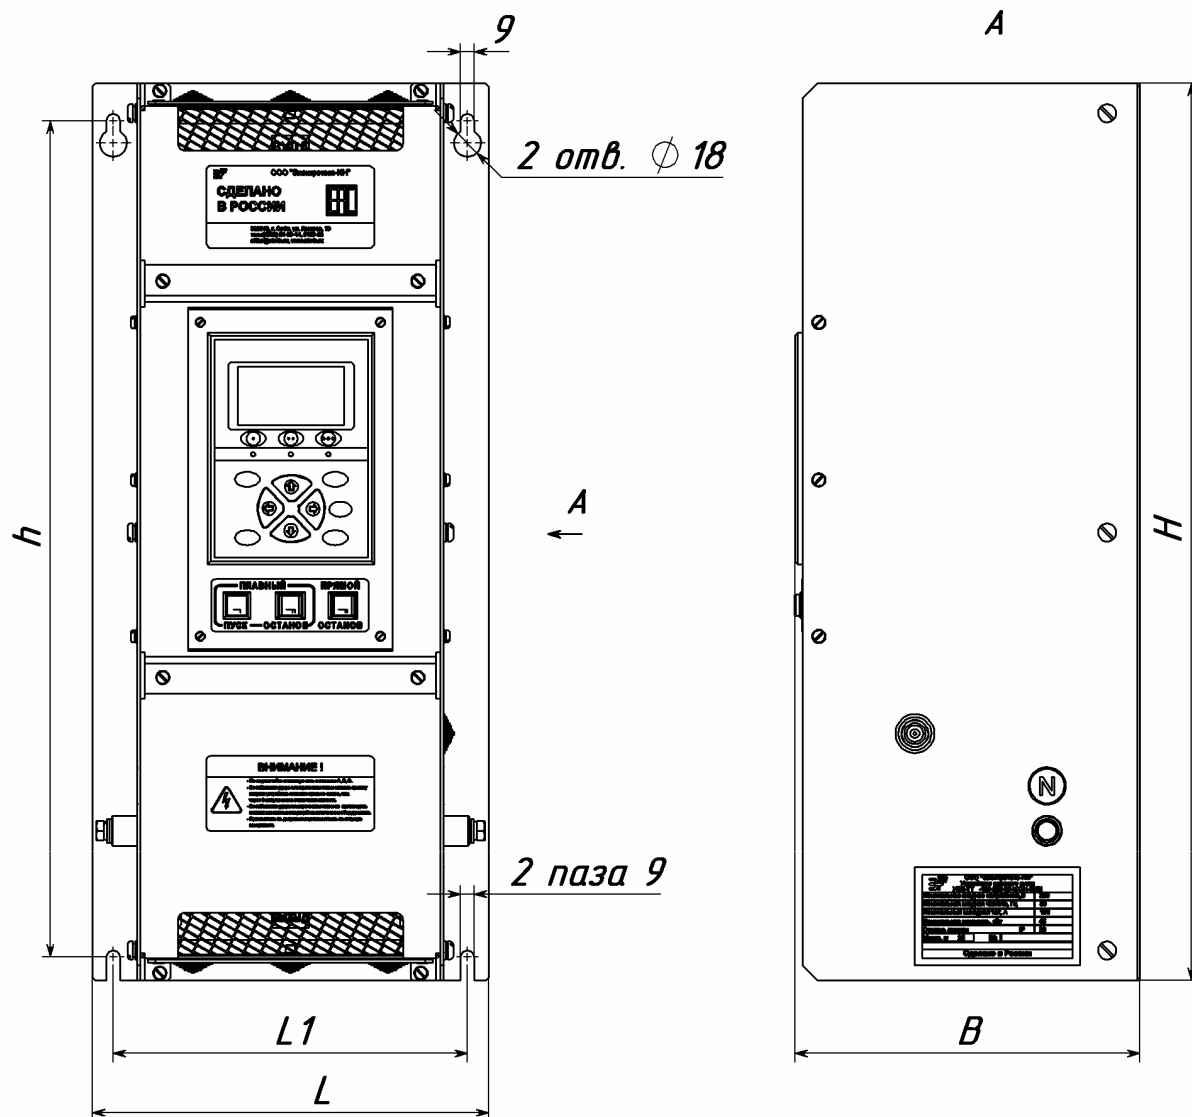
Габаритные и установочные размеры УПП 37-132 кВт
